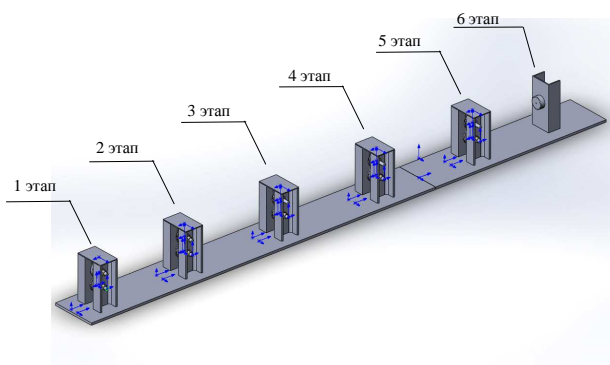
3D-модель устройства для изготовления порошковой сварочной проволоки
